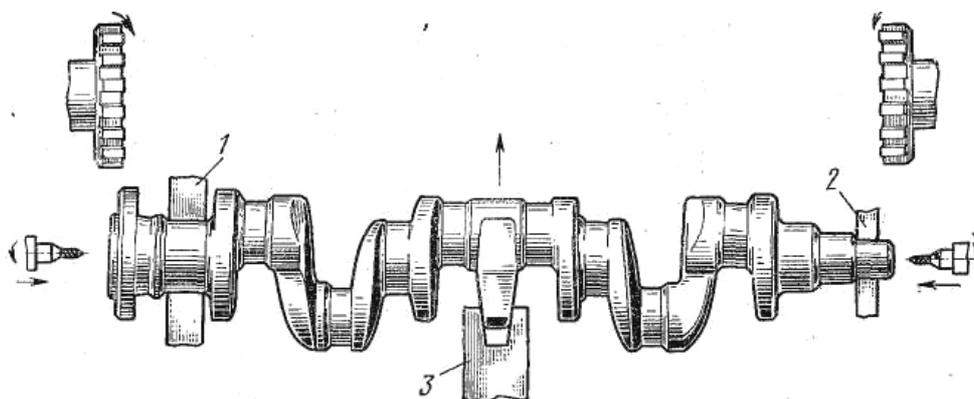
Схема обработки коленчатого вала на фрезерно-центровальном станке
